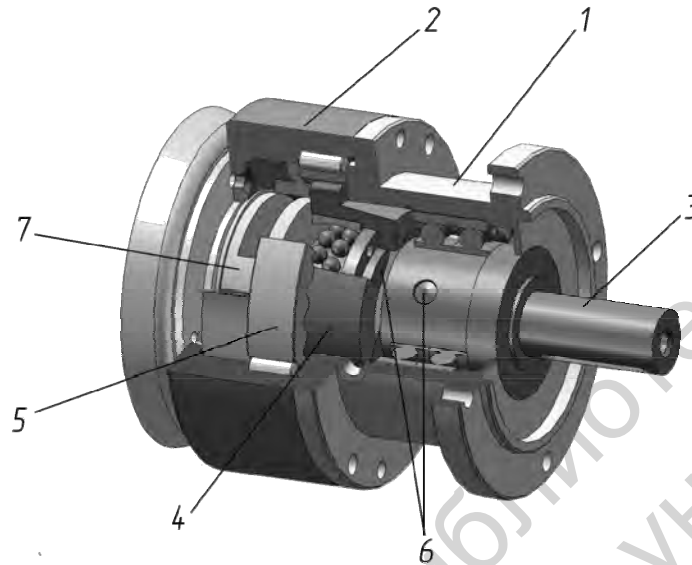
Сборочный чертеж прецессионного мотор-редуктора
